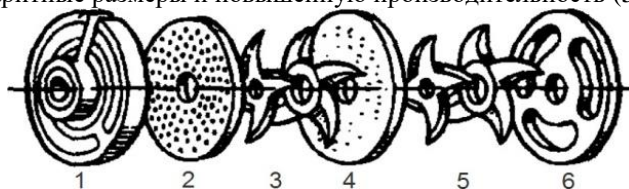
Режущий механизм волчка К7-ФВП-160-2:
